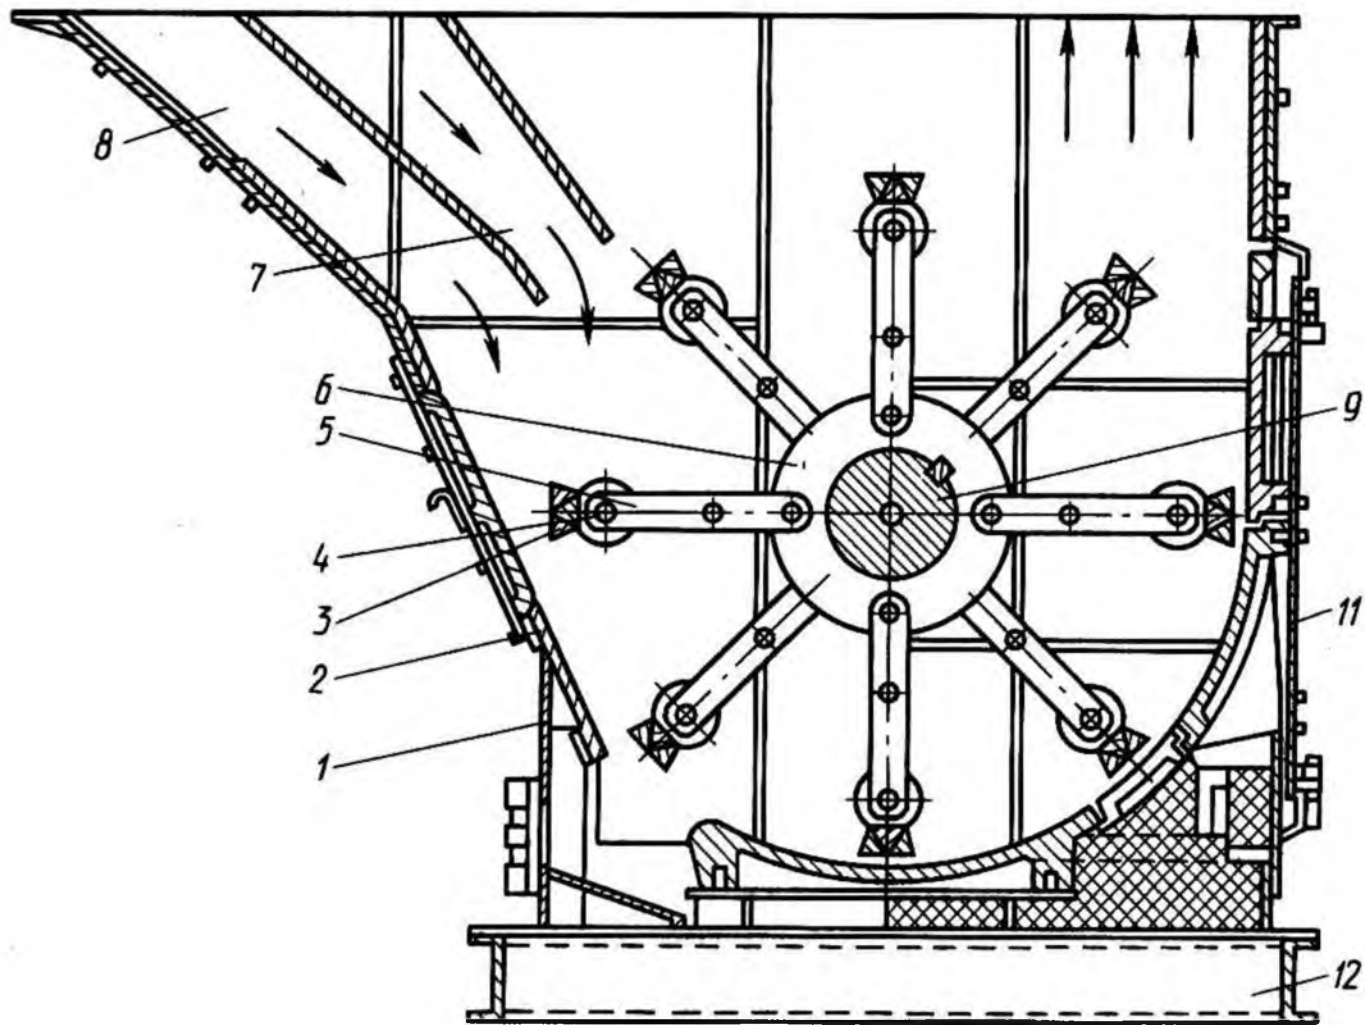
Внешний вид молотковой ударно-отражательной дробилки со сварной станинниной
